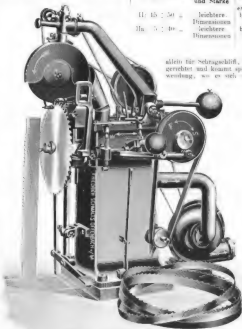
Selbsttätige Sägeschrüpfmaschine.
